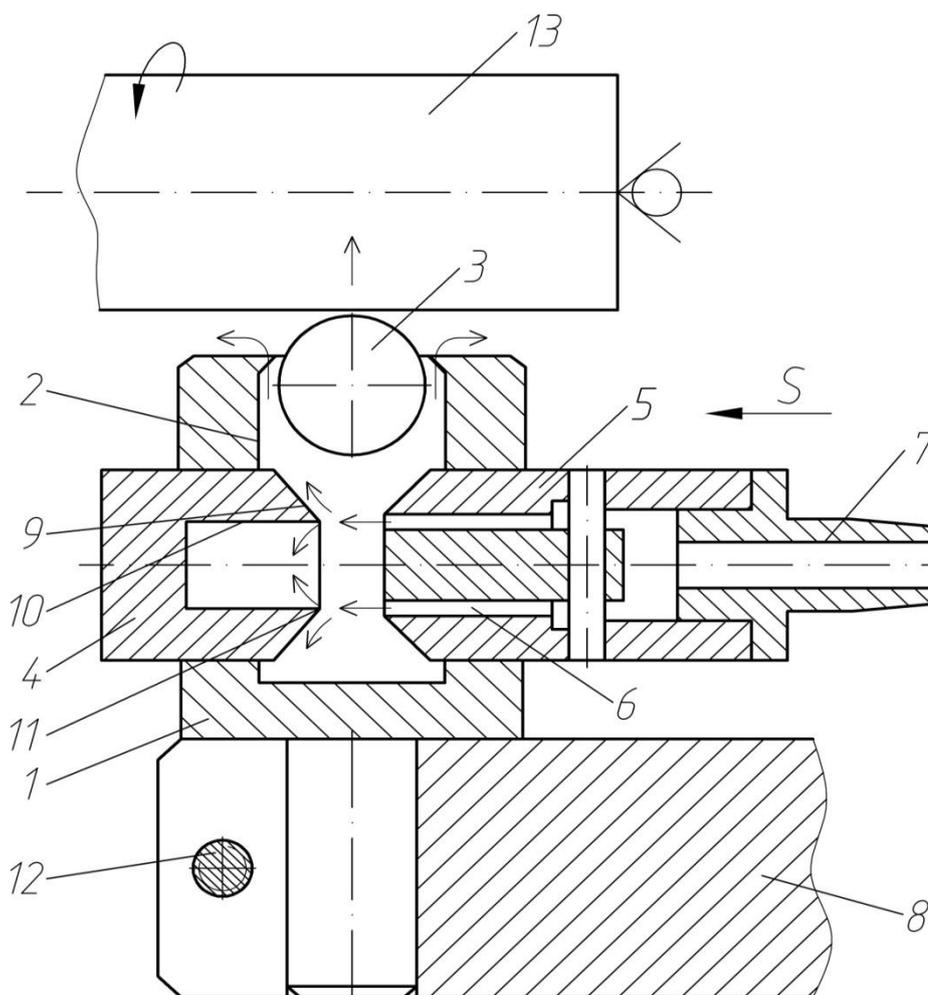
Конструкция упрочняющего инструмента с генератором ультразвуковых колебаний деформирующего шара
